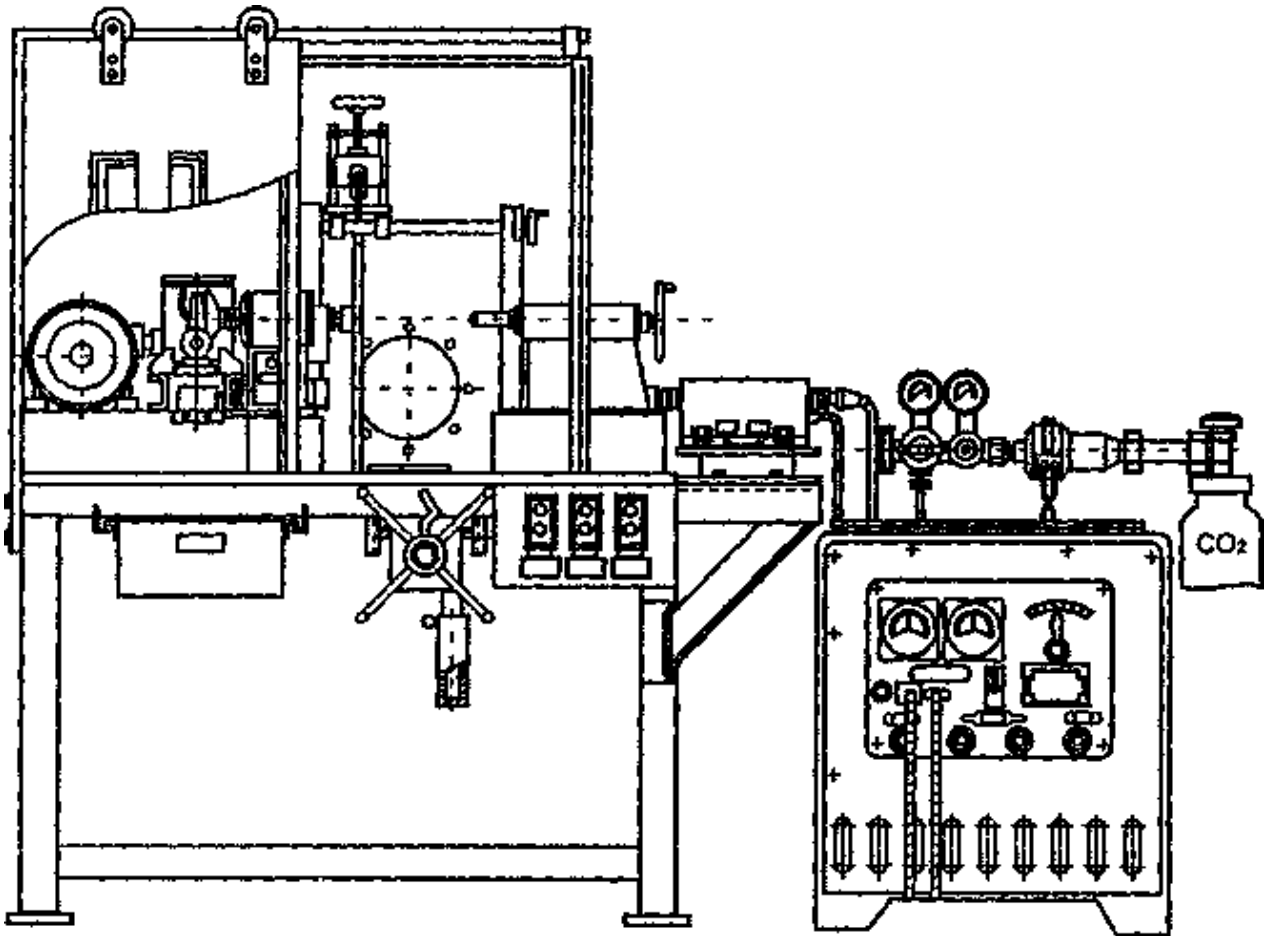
Верстат ССК-1 для зварювання кожуха мотор-компресора холодильного агрегату
